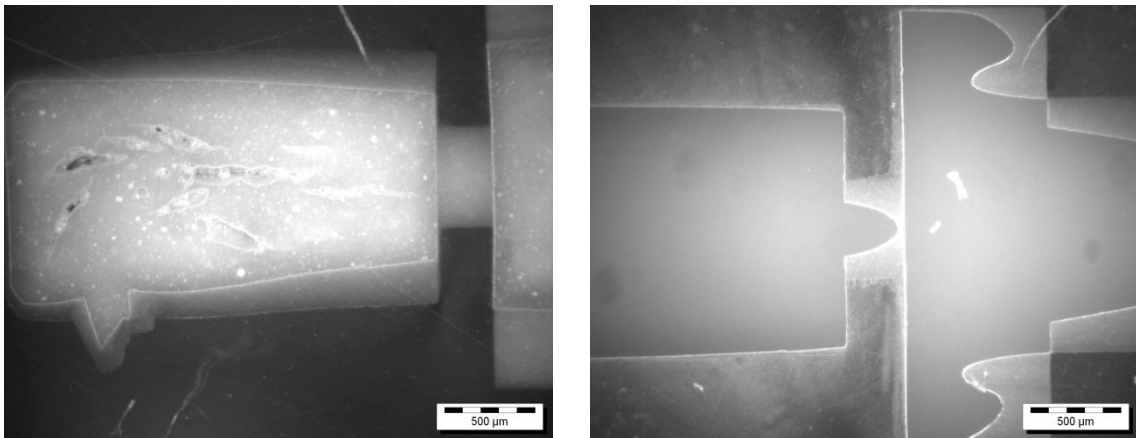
Querschliffe gesinterter, einkomponentiger Welle-Nabe-Verbindungen aus Al_2O_3 (links) und ZrO_2 (rechts).
